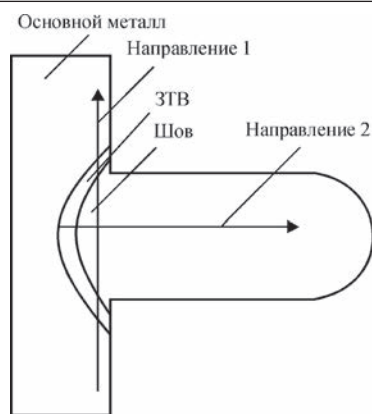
Схема измерения микротвердости наплавленного металла прямолинейной детали, изготовленной электронно-лучевой 3D-наплавкой
